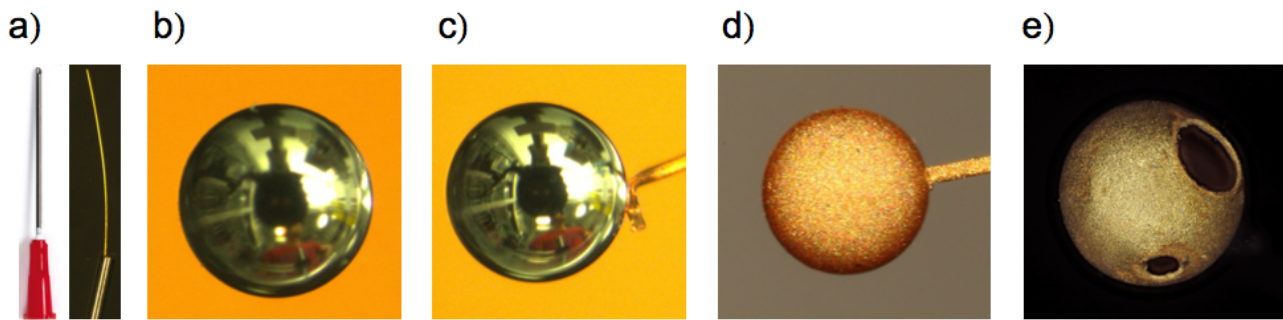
Fabrikationsschritte Primärhohlraum: Eine als Positivform dienende Stahlkugel b) wird an einen leitfähigen Draht a) geschweißt c). Nach dem galvanischen Aufbringen einer Goldschicht (15 μm) d) werden die Löcher mit einem Laser geschnitten und der Stahl heraus geätzt e).
